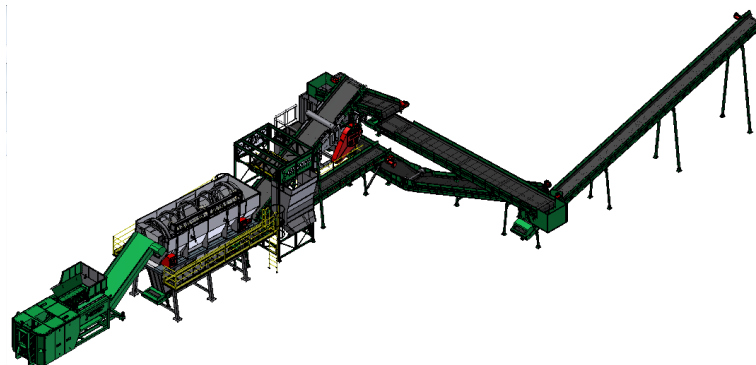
Exemplo de layout de uma planta de co-processamento de resíduos – PTBH destacado em verde.
